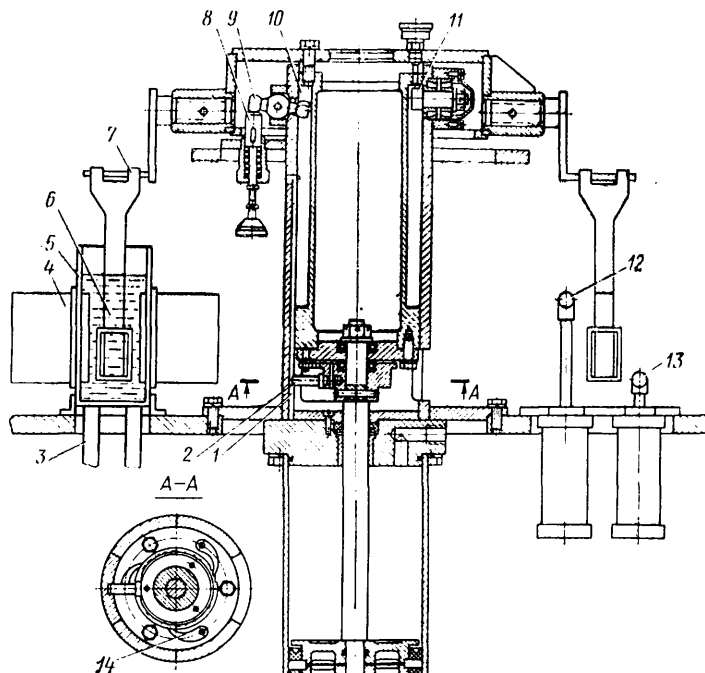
Рабочая зона установки ультразвуковой очистки деталей
